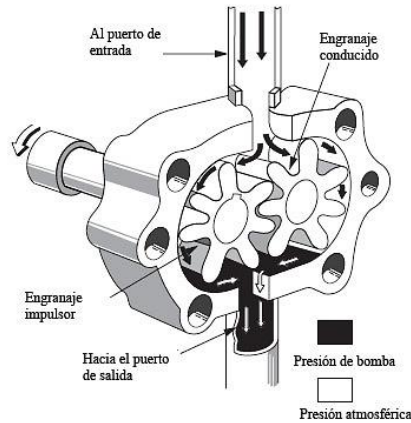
Bomba de engranajes internos y desplazamiento positivo
